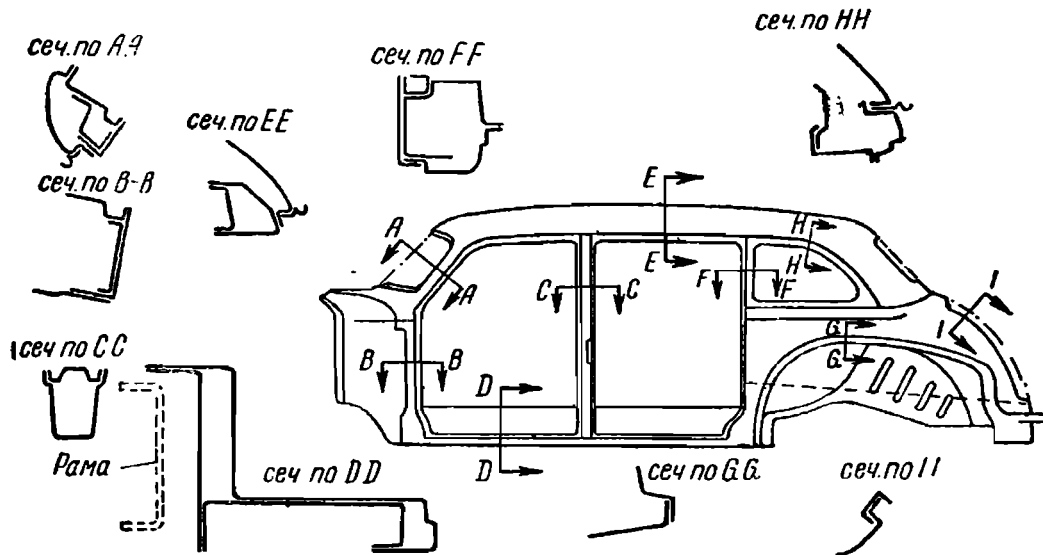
Корпус кузова автомобиля „Москвич“:
